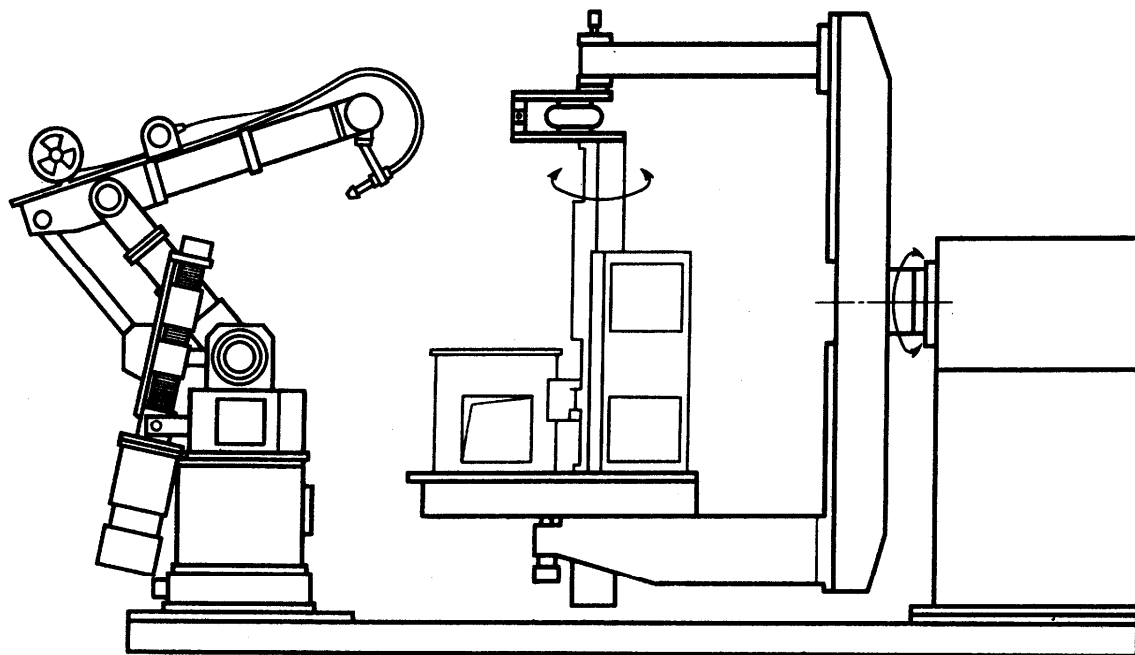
Сварка роботом печи, установленной на вращателе
